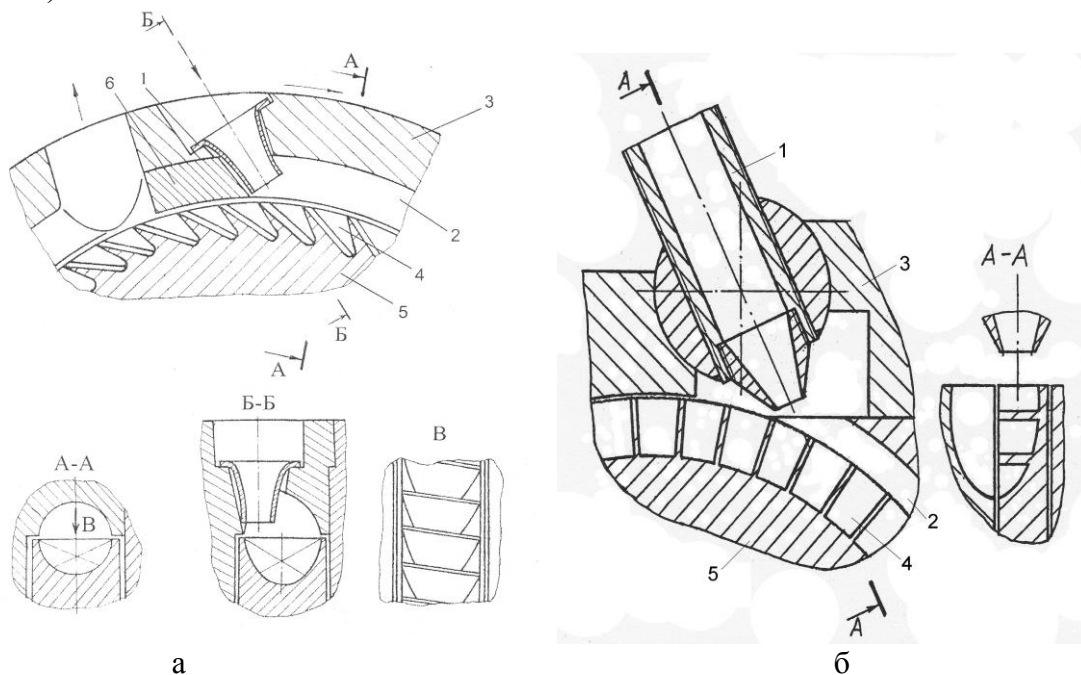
Конструктивна схема вихрового ступеня:
